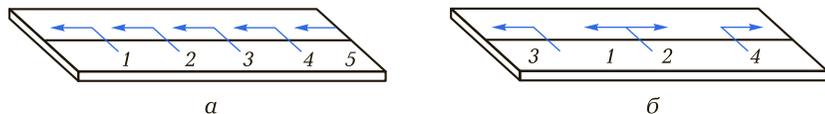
Схема обратно-ступенчатой сварки:
